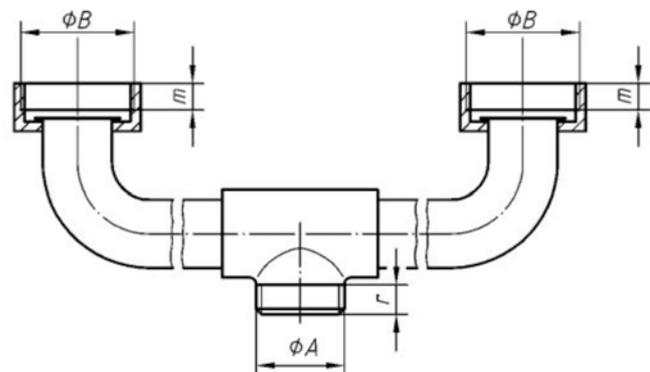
Ablaufverbindung für Küchenspüle mit zwei Becken
